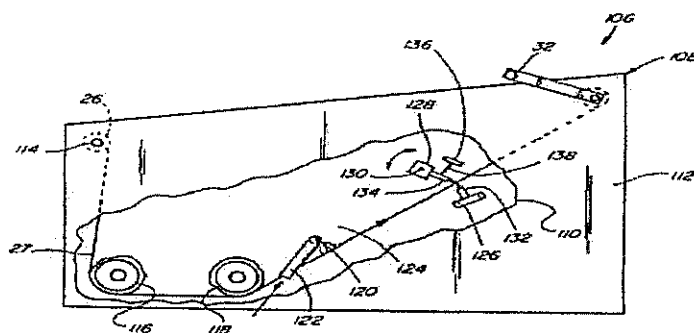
ภาพ Partial Section จากมุมมองด้านหน้าของเครื่อง Plastic Sheet Cleaning Machine
